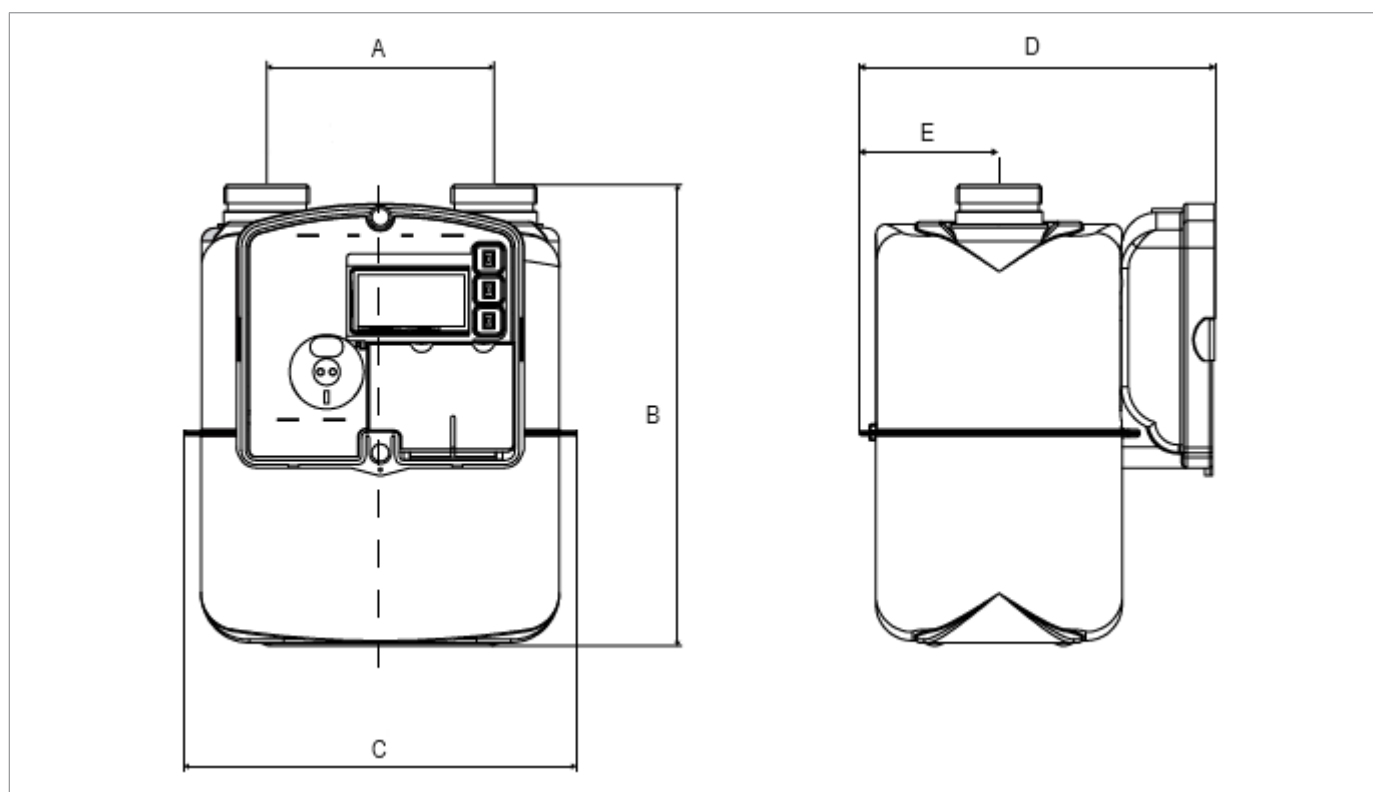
Dimensiones RSE - RSV (1.2 LA)
